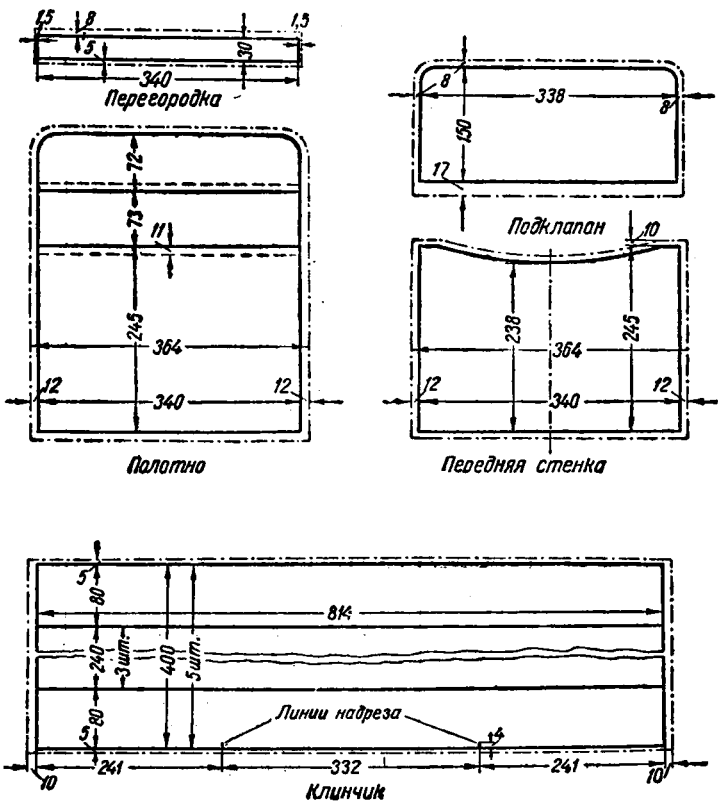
Чертеж деталей портфеля размером 32 × 24 см
